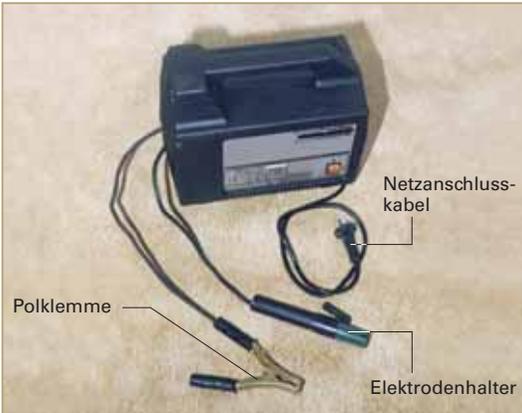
Schweißtransformator (Kleinschweißgerät)
